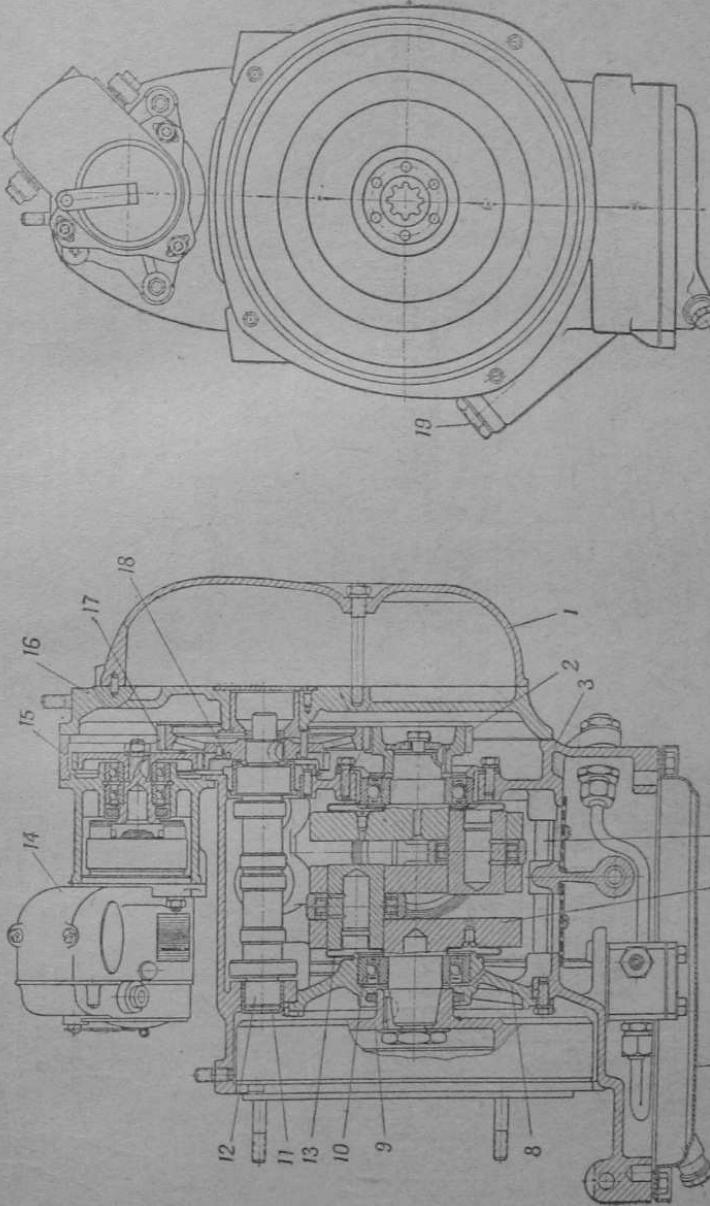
Двигатель мотоцикла М-76: слева — продольный разрез; справа — вид сзади:
